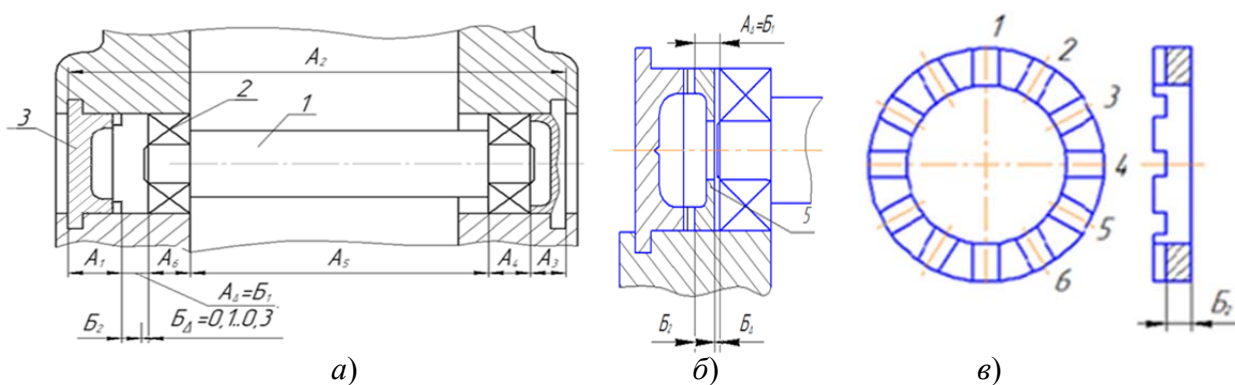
Общий вид узла редуктора с подшипниками качения (а): 1 – промежуточный вал; 2 – подшипник; 3 – крышка с выступами), эскиз узла после установки компенсатора (б); основное кольцо с пазами (в)
